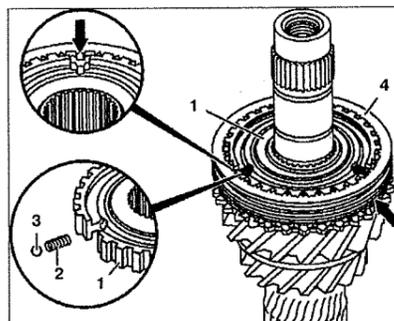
Разборка и сборка механизма включения 3-й и 4-й передач:
